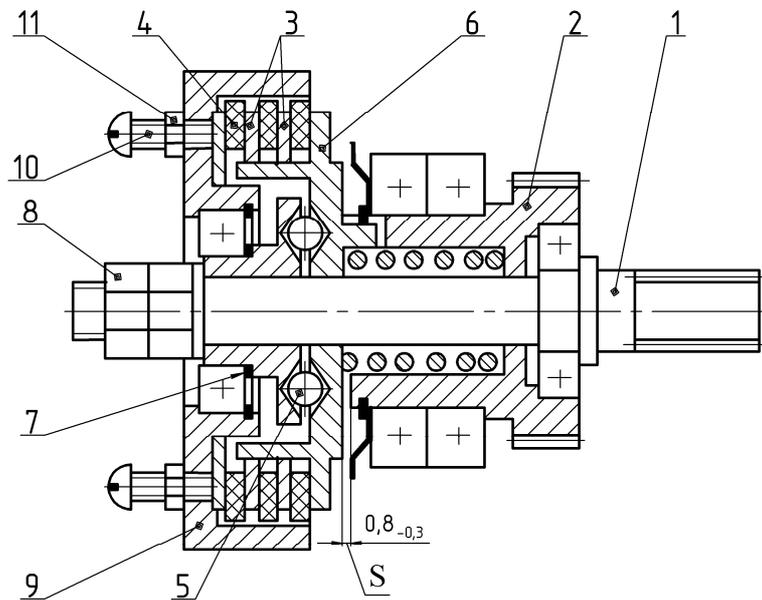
Тормоз (кроме механизма МЭП-16000/63-63)
